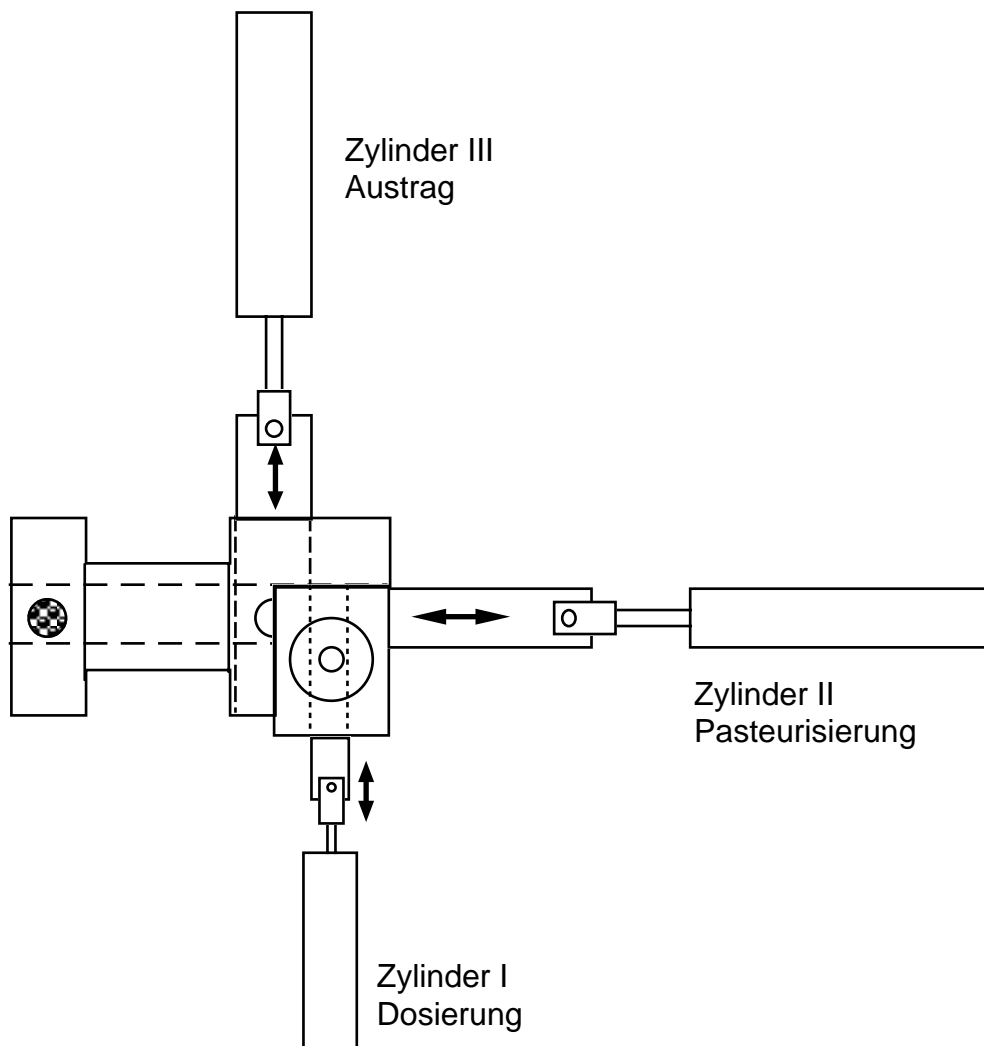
Draufsicht des Reaktorblocks mit Pneumatikzylindern.
